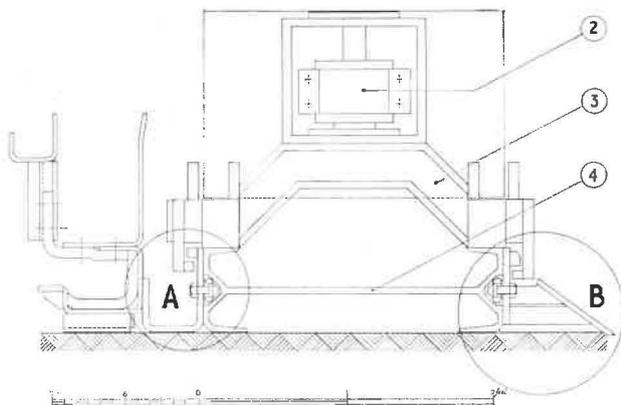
Rampe de chargement fixée sur la face frontale du convoyeur blindé.
